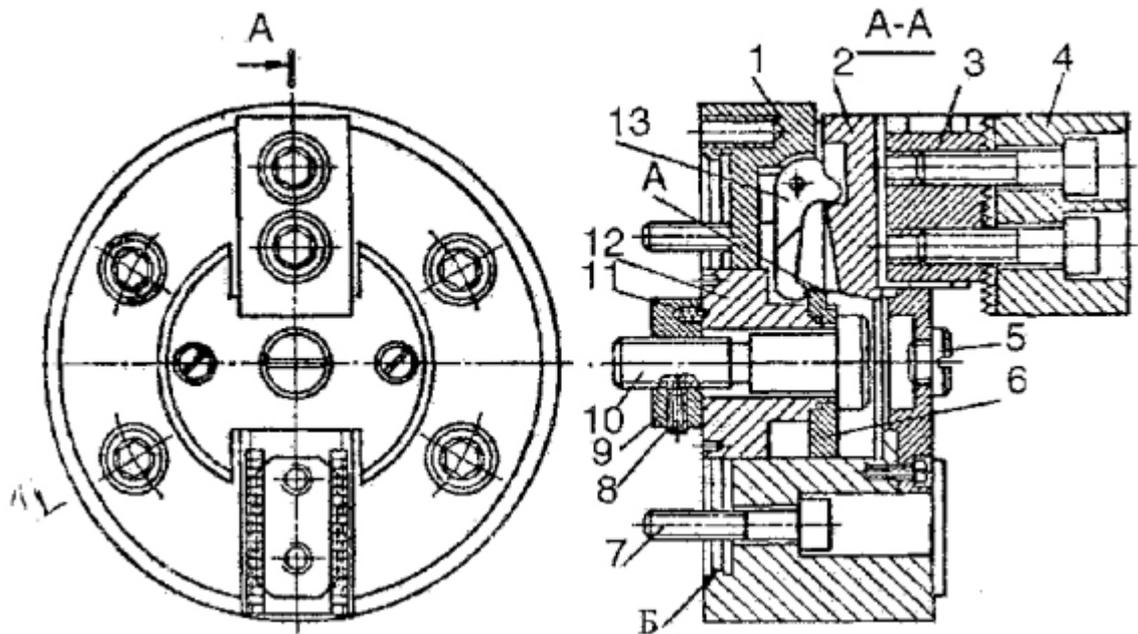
Конструкция клинорычажного двухкулачкового самоцентрирующего патрона с пневмоприводом; 1 – корпус; 2 – основания кулачков; 3 – сухари; 4 – сменные кулачки; 5 – заглушка; 6 – гайка; 7 – болт; 8 – стопорный винт; 9 – гайка; 10 – винт; 11 – шариковый стопор; 12 – втулка; 13 – рычаг.
